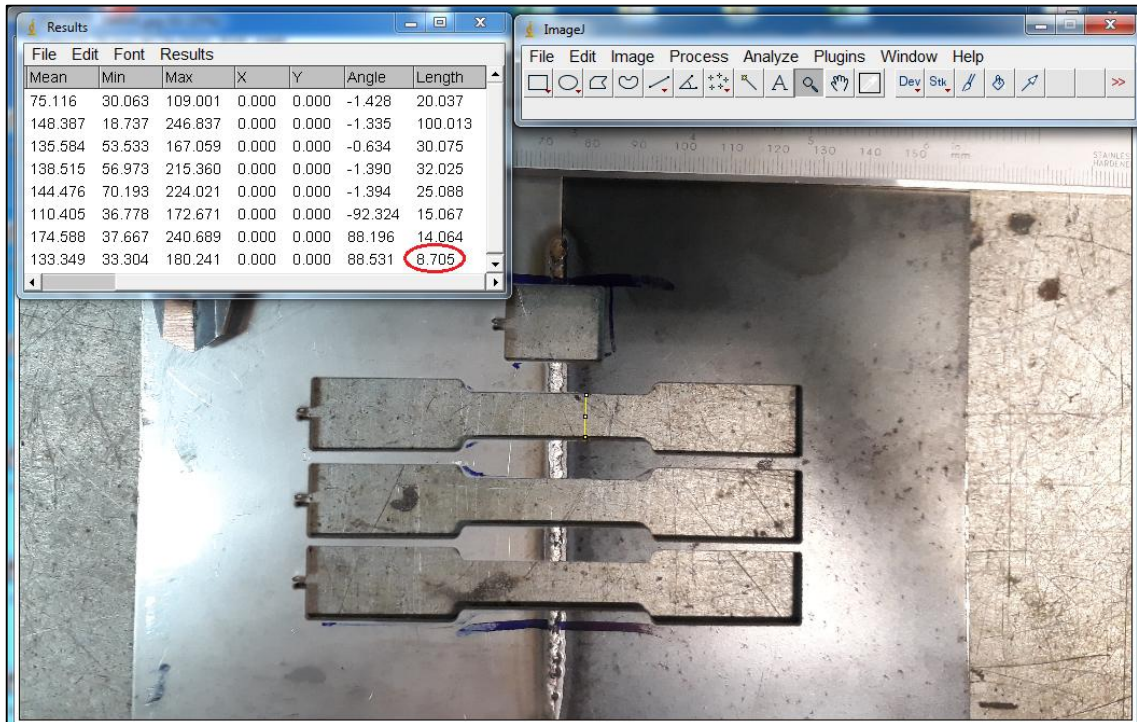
Retirada dos corpos de prova a partir das juntas soldadas.
